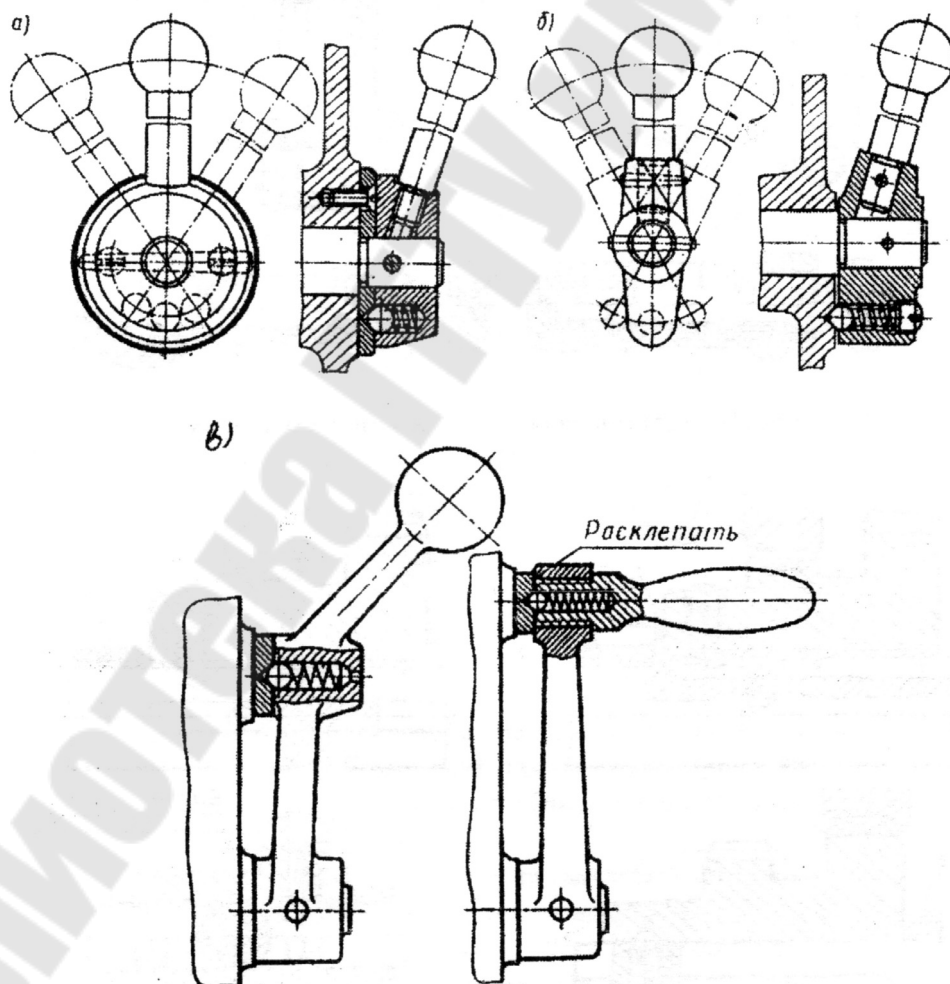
Конструкции рукояток управления с шариковым фиксатором.
